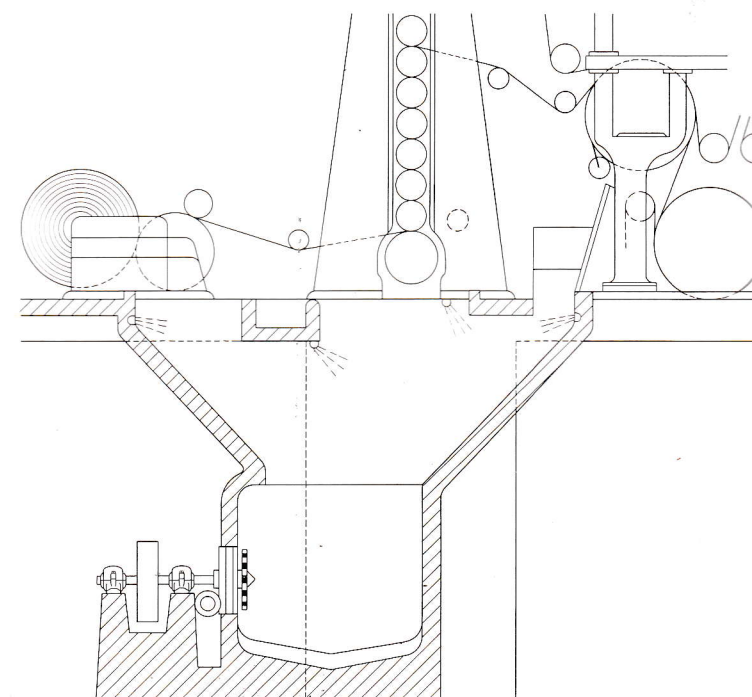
Desintegrador horizontal para papel de desecho colocado debajo del grupo de acabado de una máquina rápida de papel
